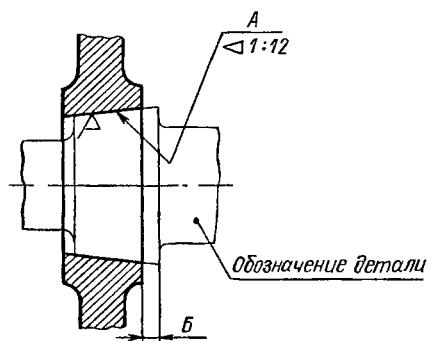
Чертеж детали, обрабатываемой по другой детали
